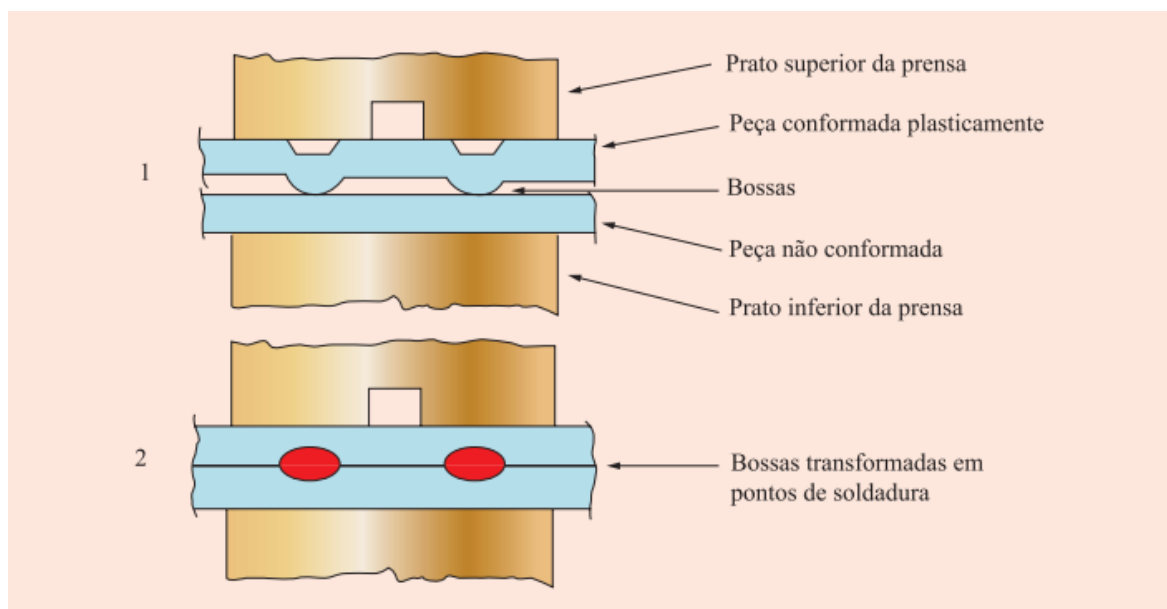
Princípio de soldadura por projeção (Retirado de: Silva, 2016)
